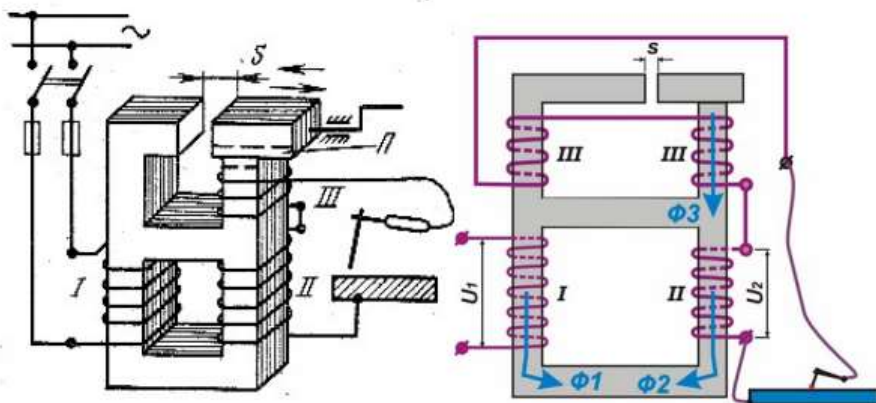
Схема сварочного трансформатора типа СТН
